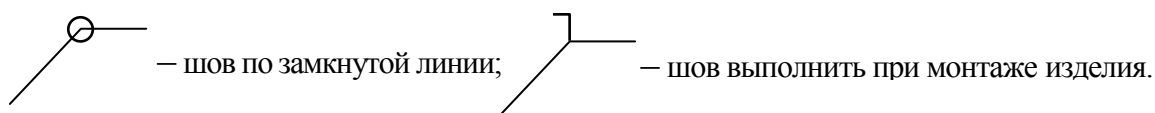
Структура условного обозначения сварного шва
